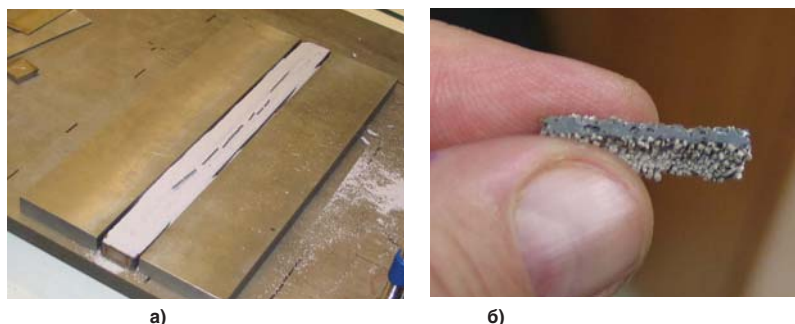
Шлаковая корка отставала практически без применения механического воздействия — а, и имела оплавленную поверхность, аналогичную шлаковой корке при дуговой сварке под флюсом (б).
